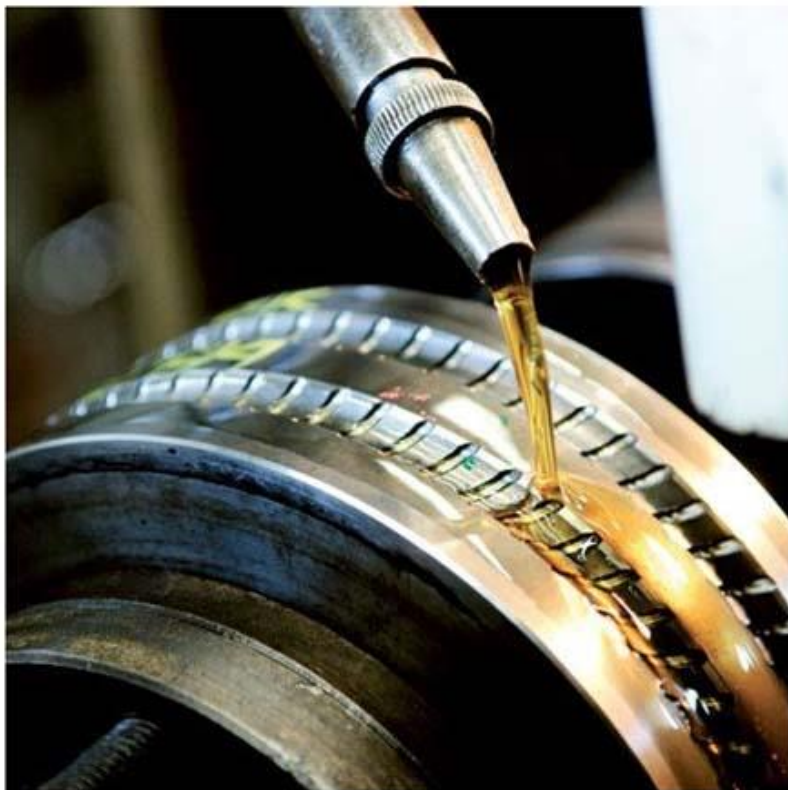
Процес нанесення змашувальної рідини на поверхню деталі з трибоз'єднання [3].
